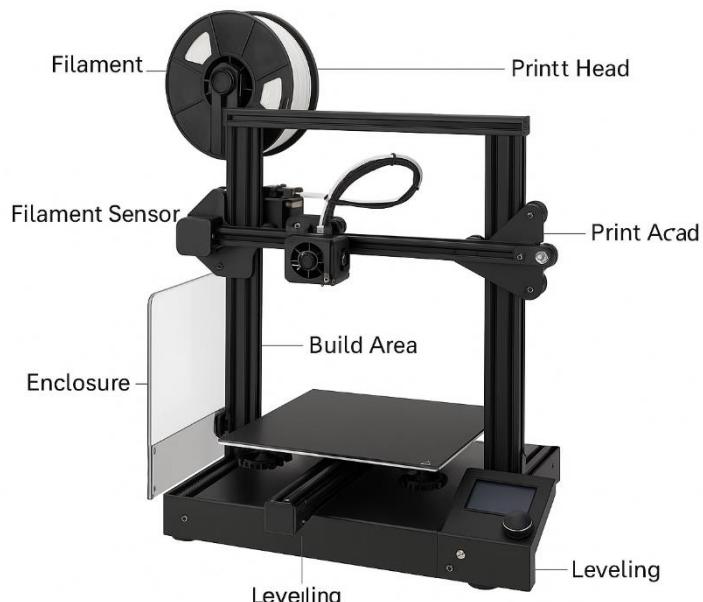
Partes de una máquina de impresora 3D FDM. Open IA (2025).
